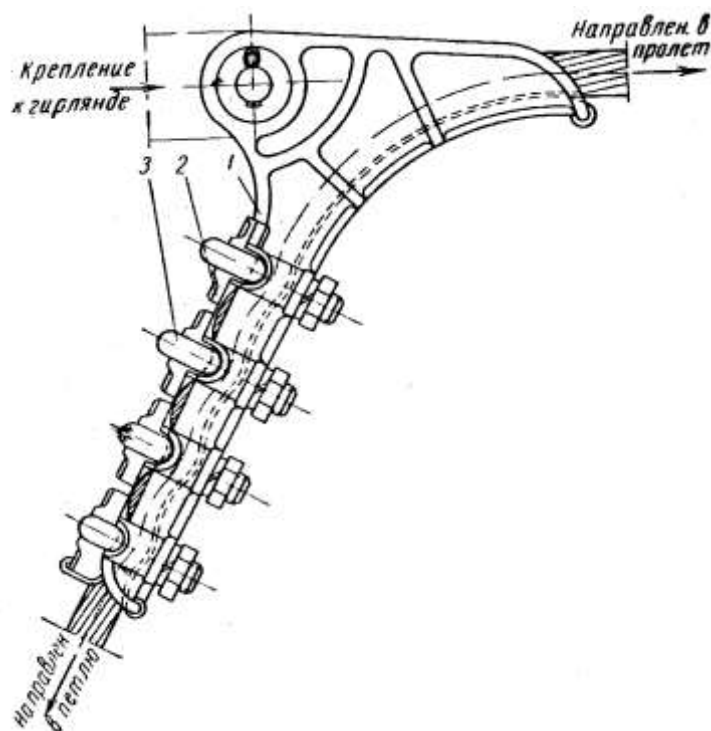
Натяжной болтовой зажим новой конструкции типа НБ-2-6
